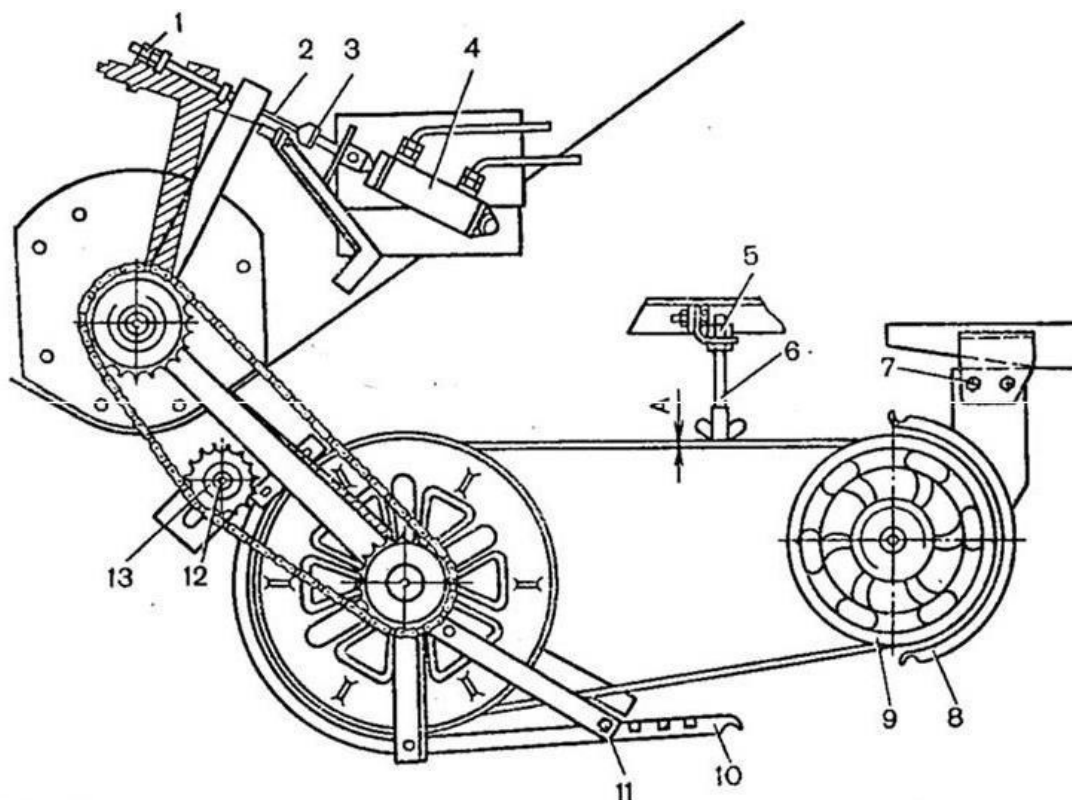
Регулировка механизма включения выгрузного устройства:
